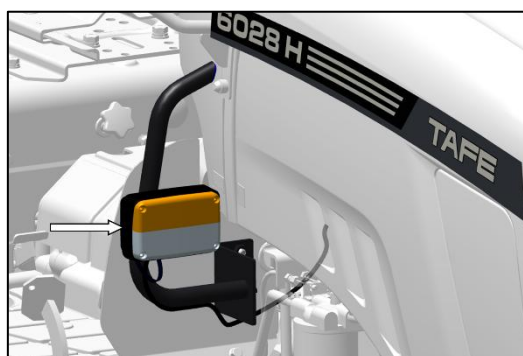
REMPLACEMENT DE L'AMPOULE DU CLIGNOTANT AVANT
